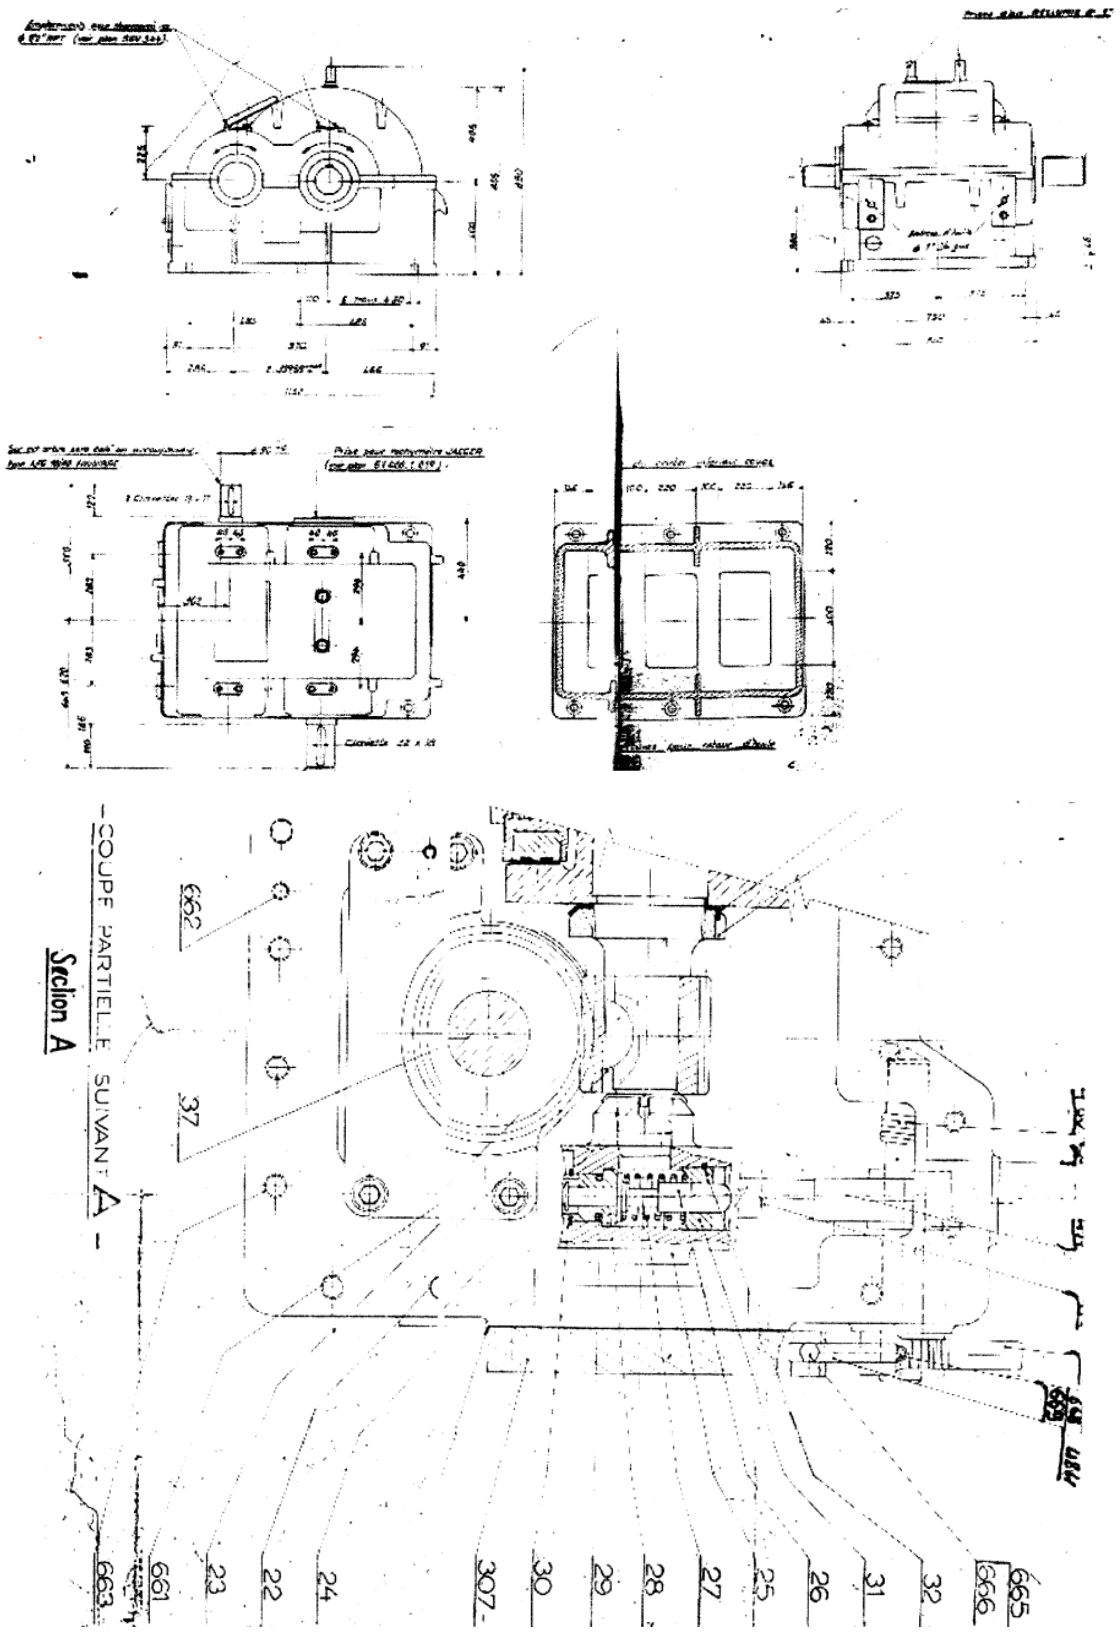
Dessin d'ensemble en coupe de la turbine à vapeur.
